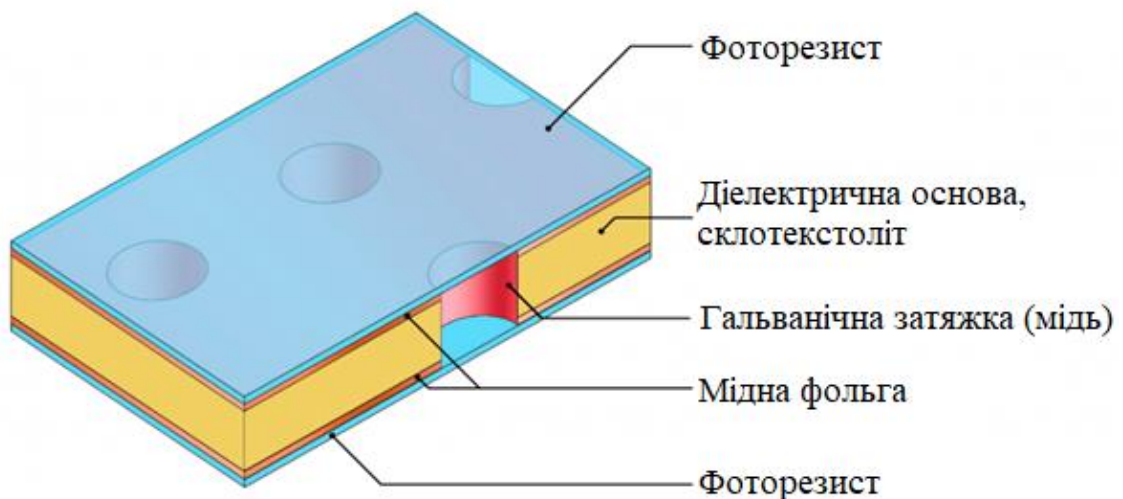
Вигляд плати з нанесеним фоторезистом
